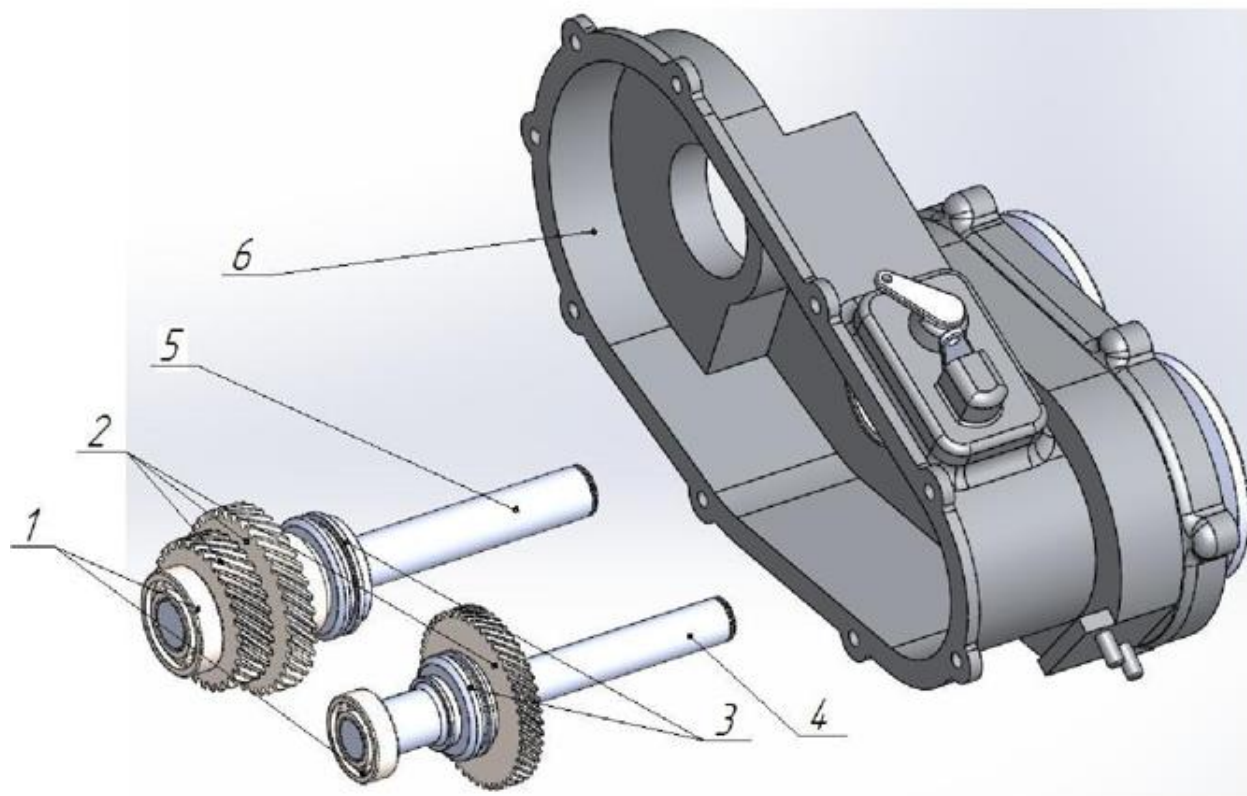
Ведущий и ведомые валы: 1 – подшипники качения; 2 – зубчатые колеса; 3 – зубчатые муфты; 4 – ведущий вал; 5 – ведомый вал; 6 – корпус вариатора
